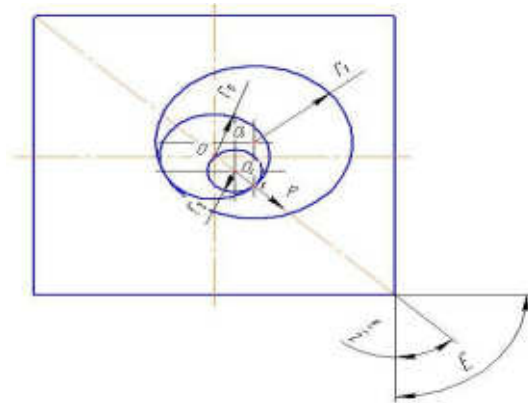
Расчетная схема эксцентрического закрепления.
